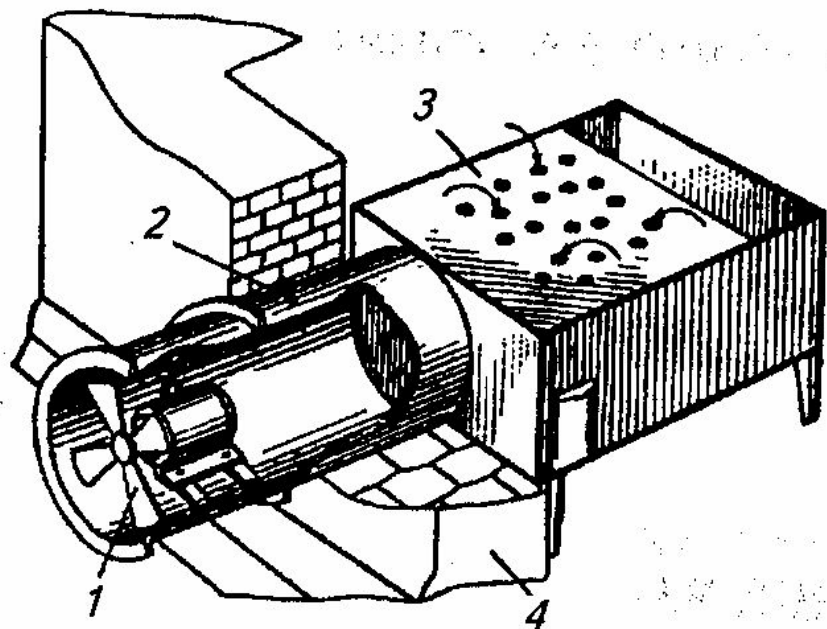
Вытяжная вентиляция на рабочем месте сварщика:
